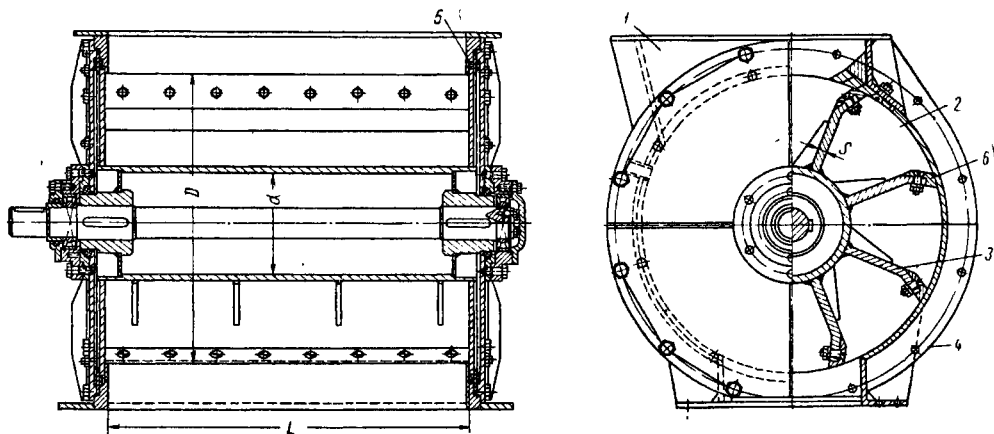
Шлюзовой питатель барабанного типа конструкции ЦНИИМЭ
